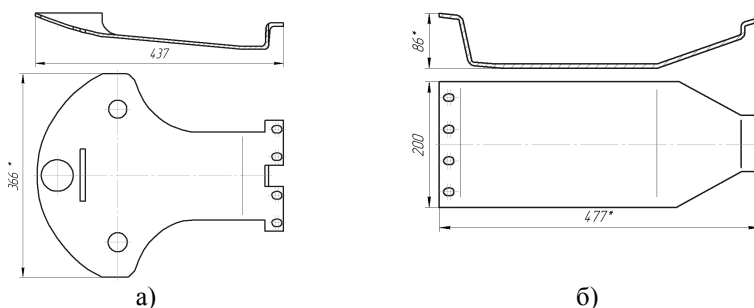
Эскизы основного (а) и дополнительного основания (б) башмака режущего бруса роторных косилок
